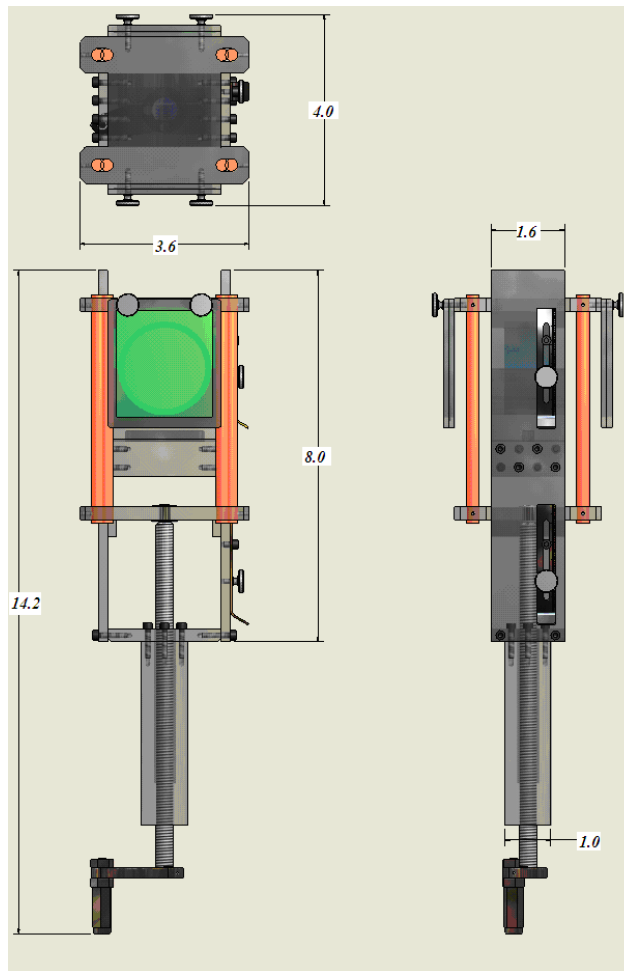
Vistas y dimensiones generales, en milímetros, del Probador Mecánico Portátil (PMP).
